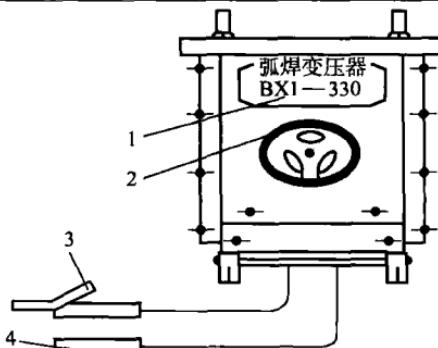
BX1—330 型弧焊变压器焊接电流的调节
